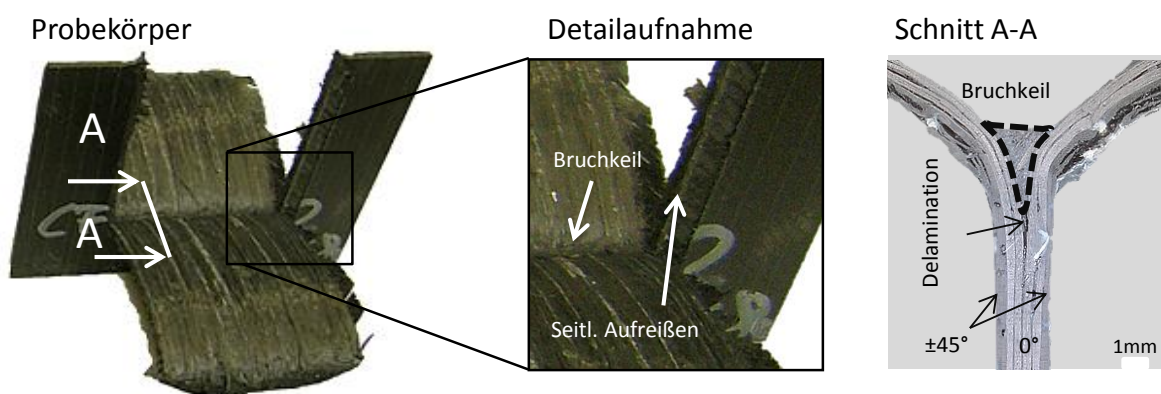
Quasi-statisch geprüfter Probekörper des MAT A inklusive Detailaufnahme (Mitte) und Schnittdarstellung der Bruchfront (rechts).
